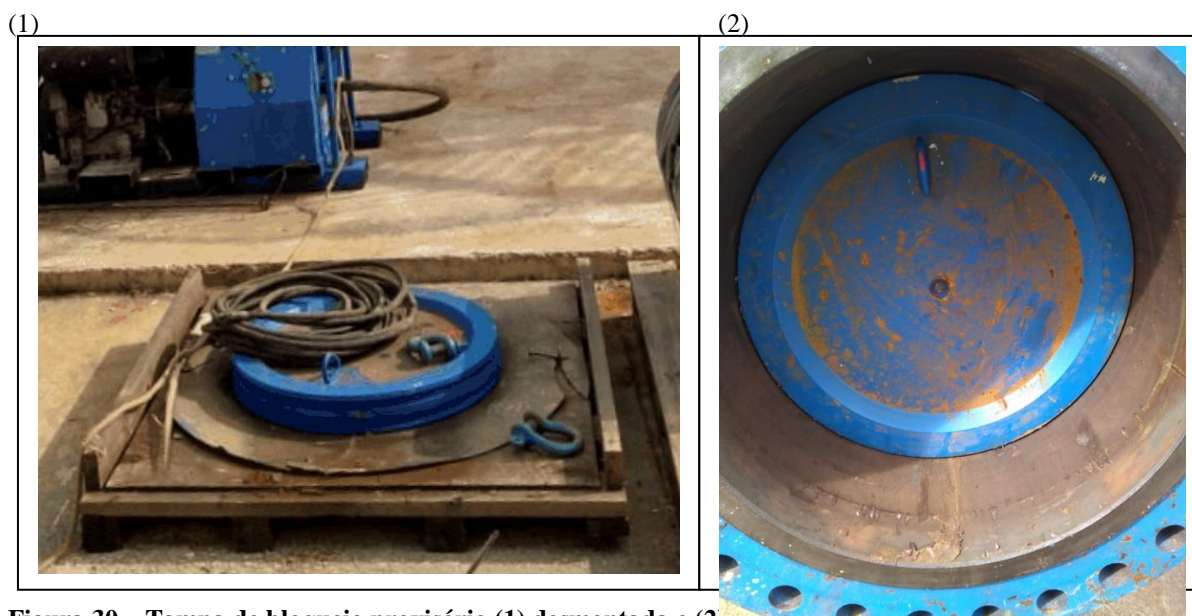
Tampa de bloqueio provisório (1) desmontada e (2) montada na ferramenta de inserção
